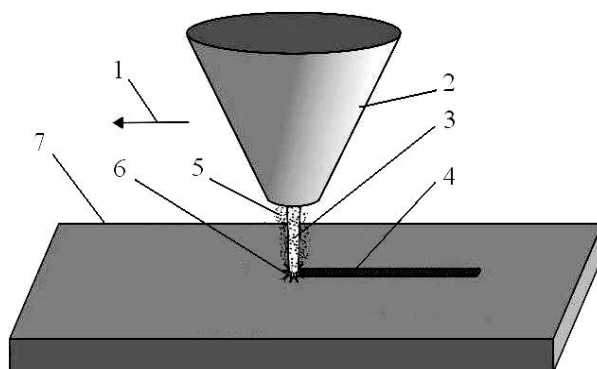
[1]. Схема способа 3D печати металлоизделий: 1 – направление движения; 2 – сопло осадителя; 3 – пучок лучей лазера; 4 – осажденный слой; 5 – частицы порошка; 6 – зона расплава; 7 – подложка.
